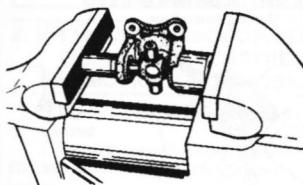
Для того, чтобы снять шарнир с карданного вала, закрепите его в тисках, поместив малый торцовый ключ (слева) для упора в шарнир, чтобы выдавить подшипник в большой торцовый ключ
